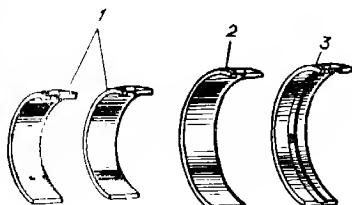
Вкладыши подшипников коленчатого вала и нижней головки шатуна:
